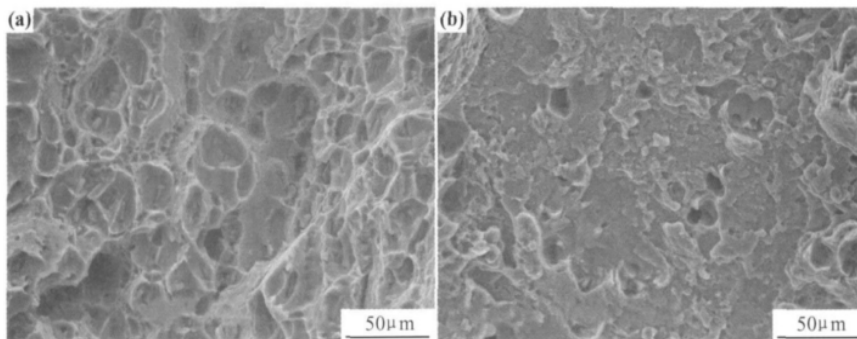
焊缝拉伸断口形貌 (a) 焊缝上部;(b)焊缝底部
